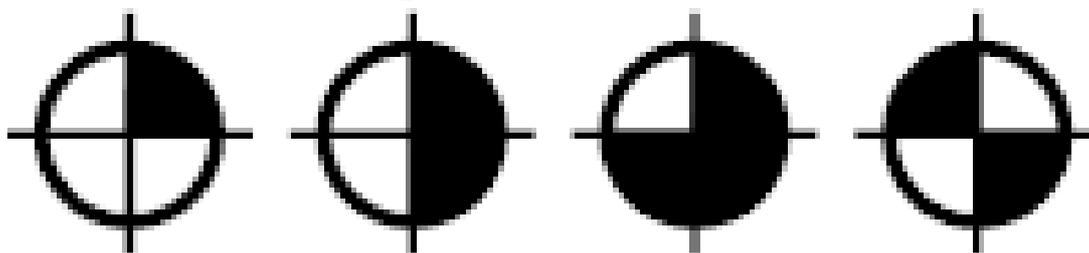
Условные знаки обозначения групп отверстий с одинаковым диаметром
